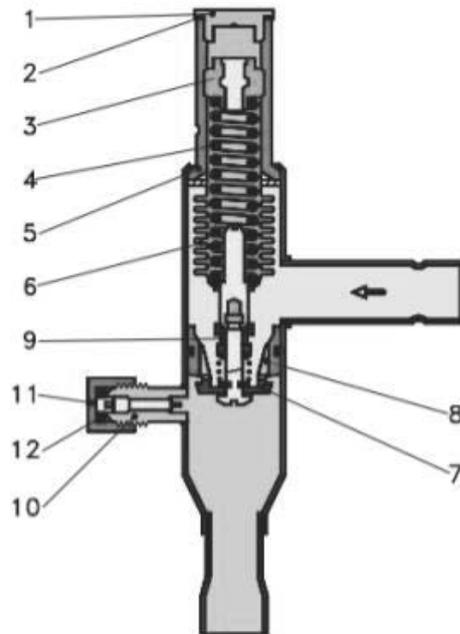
Регулятор давления KVD 15:1 – защитный колпачок; 2 – прокладка; 3 – регулировочный винт; 4 – основная пружина; 5 – корпус клапана; 6 – уравнивающий сильфон; 7 – пластина клапана; 8 – посадочное седло; 9 – демпфирующее устройство; 10 – штуцер для подсоединения манометра; 11 – колпачок; 12 – прокладка.
